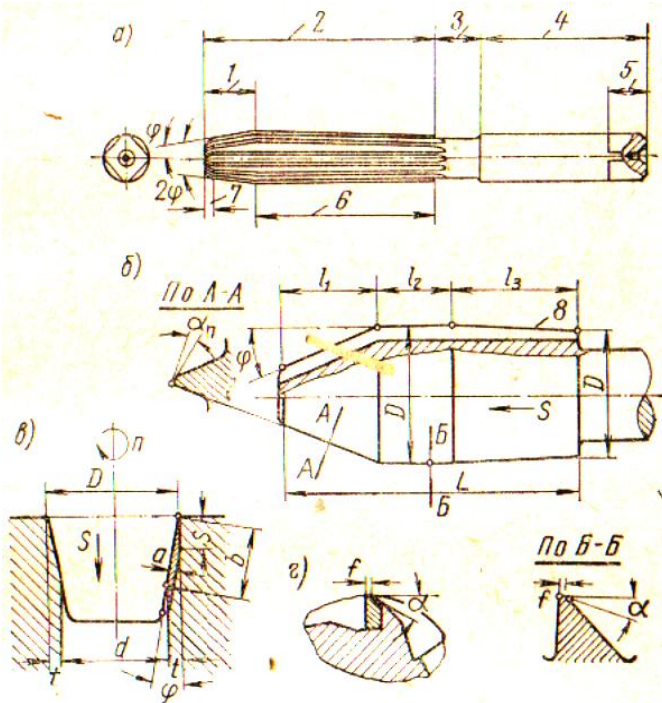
Элементы конструкции развёртки и схема резания: а – элементы конструкции развёртки; б – схема развёртки; в – схема резания; 1 – режущая часть; 2 – рабочая часть; 3 – шейка; 4 – хвостовик; 5 – квадрат; 6 – калибрующая часть; 7 – направляющая часть; 8 – обратный конус
